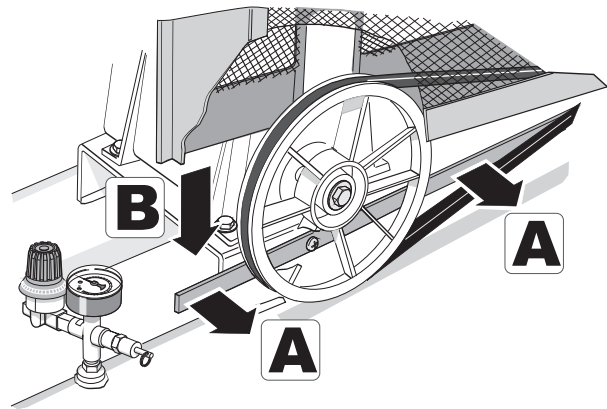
MONTAJE DEL PROTECTOR DE CORREA
